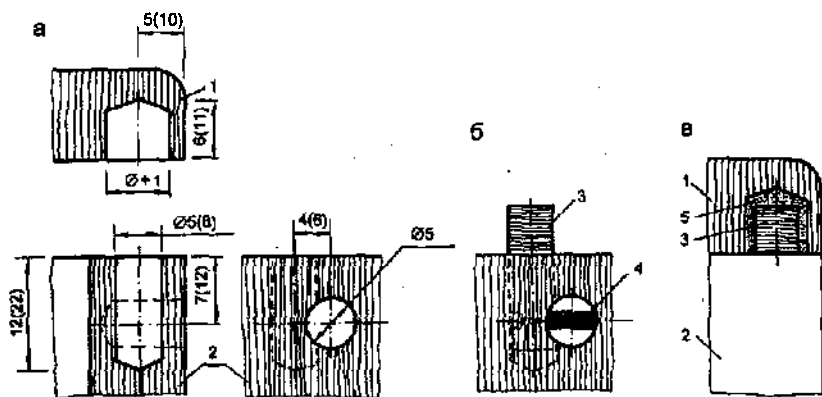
Этапы монтировки элементов шкатулки: разметка и сверление отверстий — а; фиксация шарнира в корпусе — б и в крышке — в; 1 — крышка; 2 — корпус; 3, 4 — стержень и шпонка шарнира; 5 — клей с наполнителем
